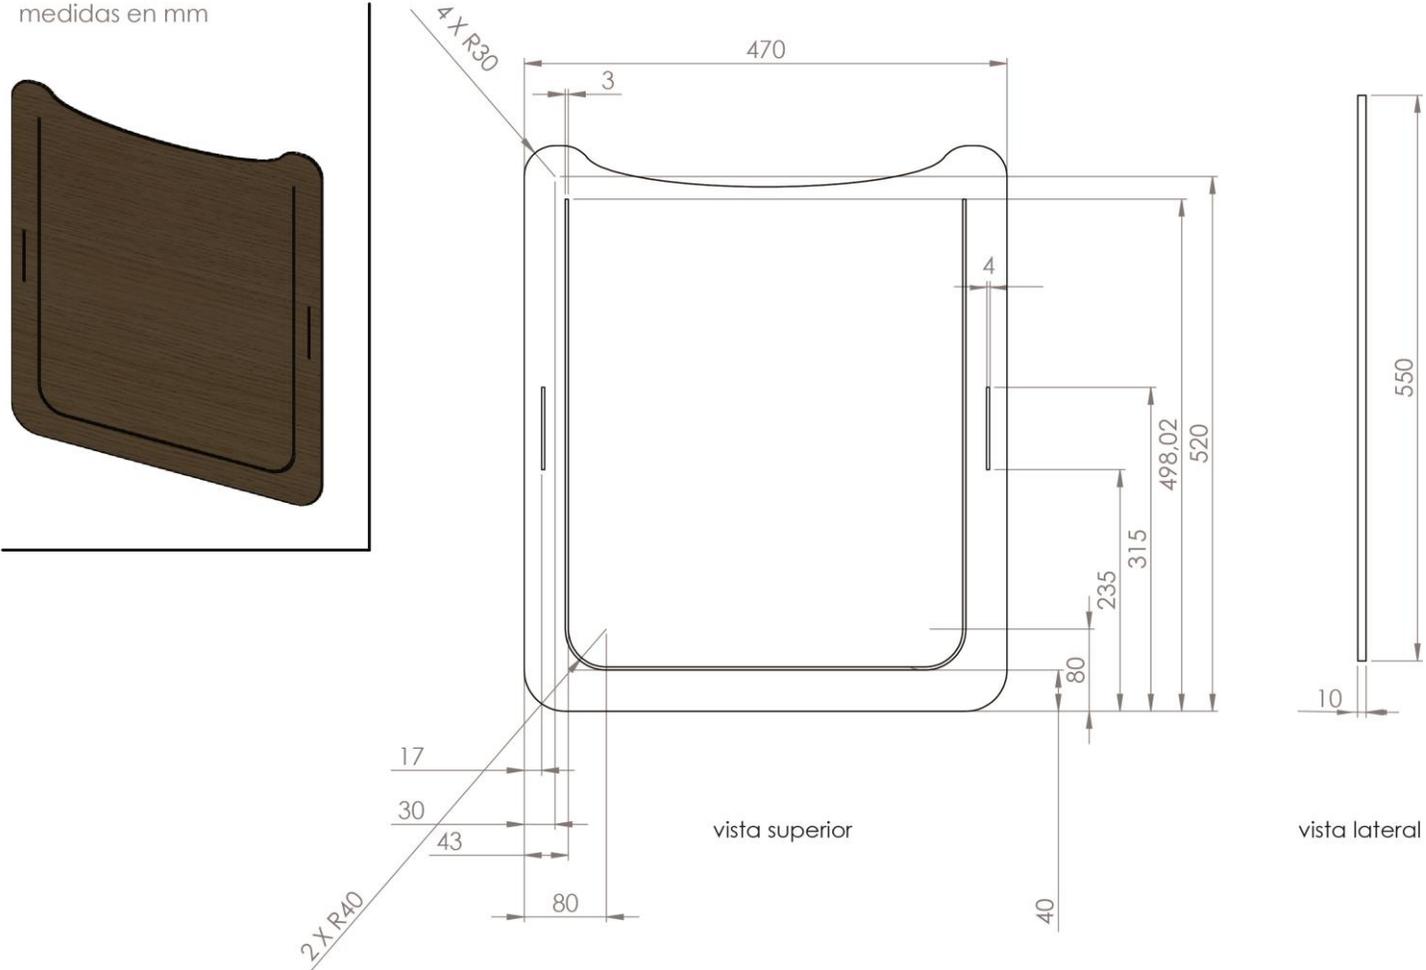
Planos en detalle del subsistema silla. Elaboración propia.
